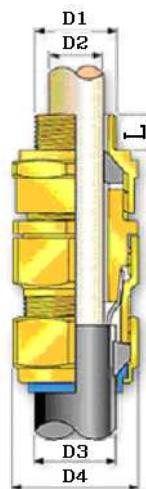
Ввод кабельный для бронированного стальной проволокой кабеля (К4)
